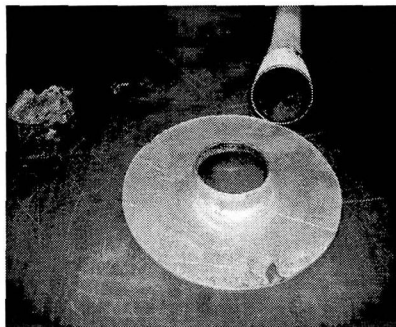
Полученная отбортовка при штамповке с нагревом и толкатель в виде трубы
